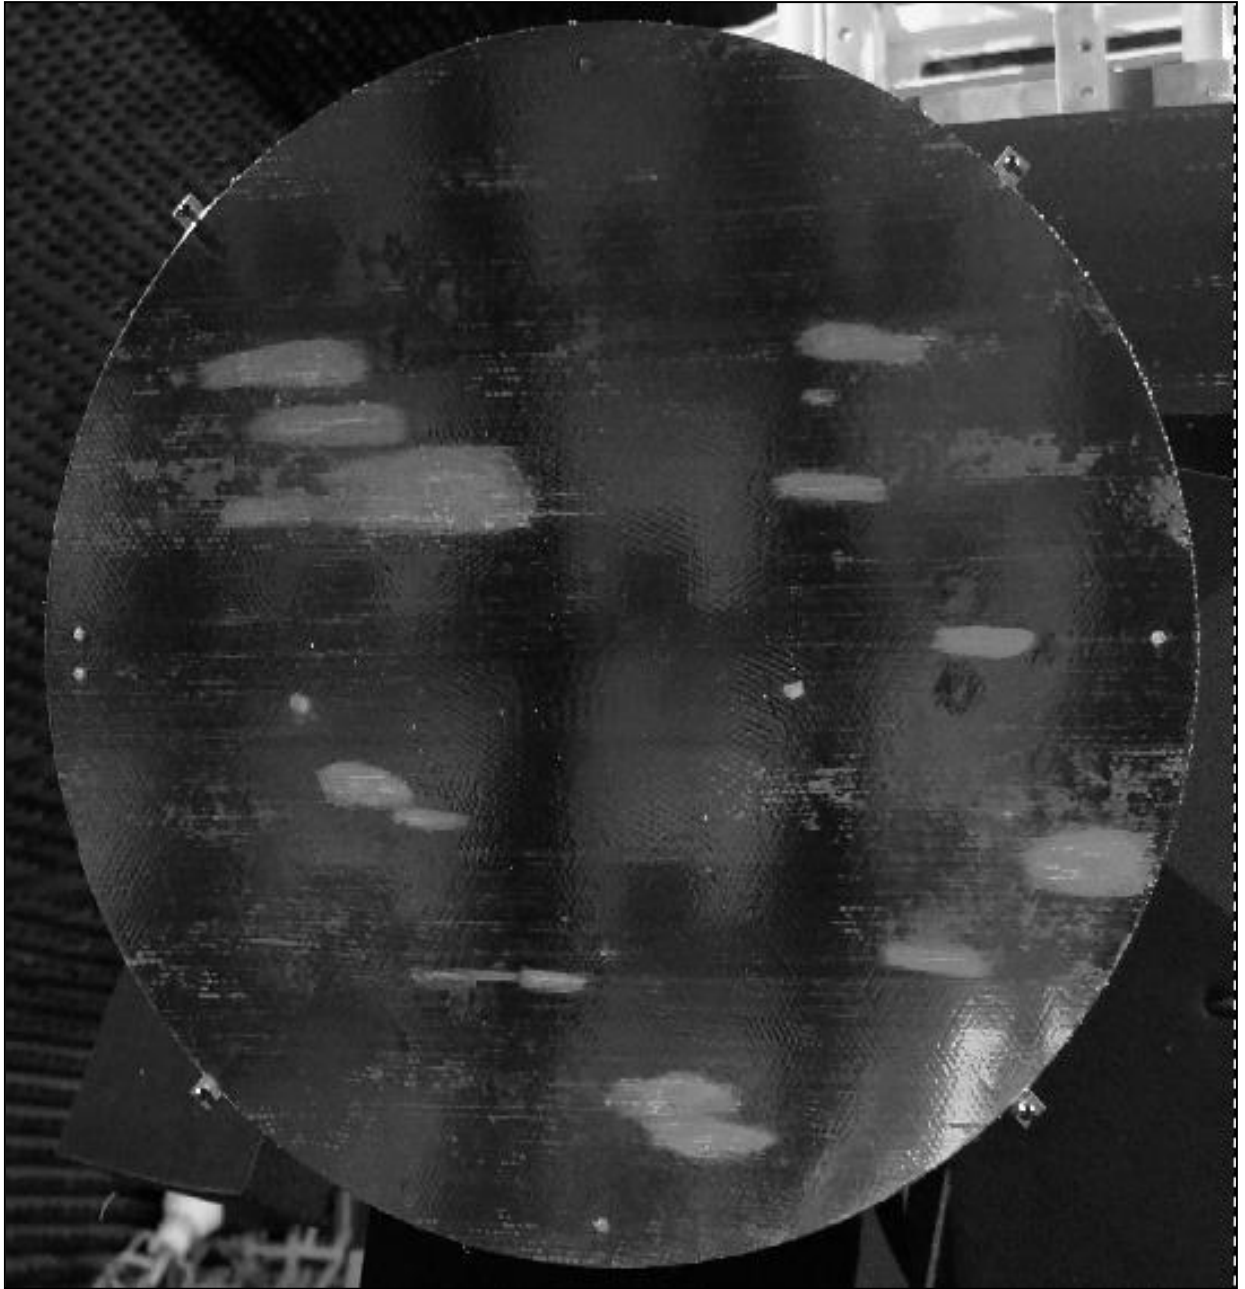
Внешний вид рефлектора с неоднородностями поверхности
